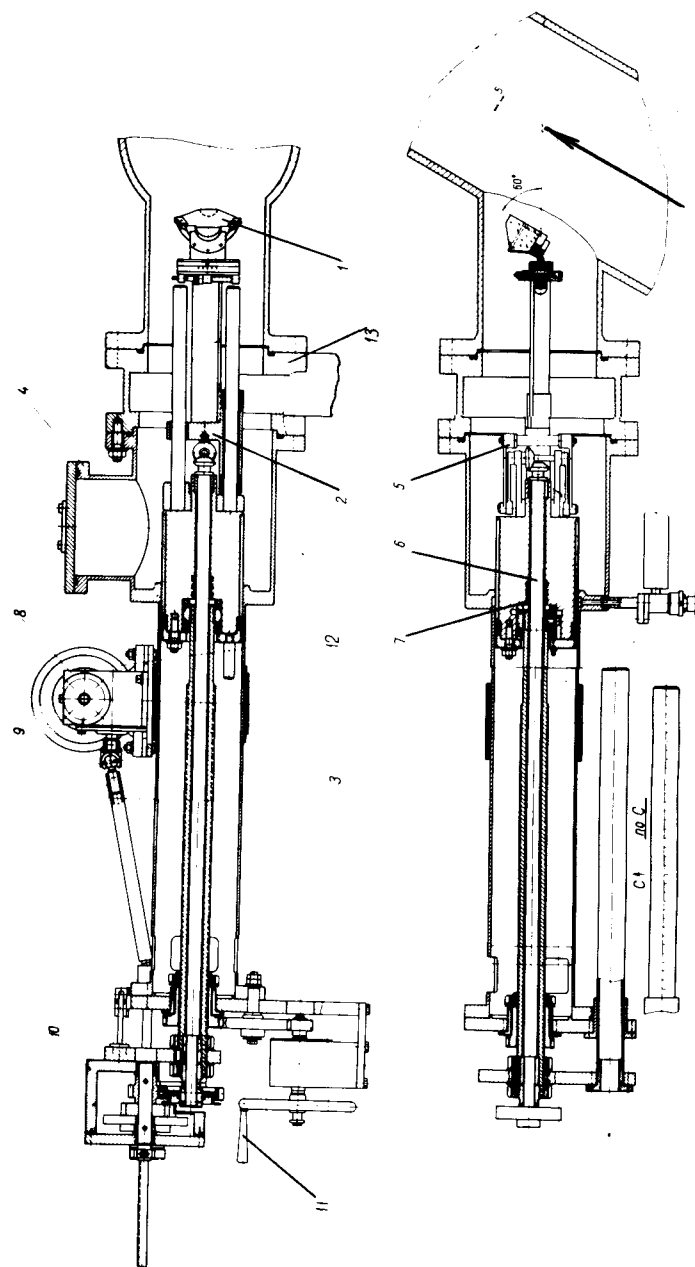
Механизм ввода мишени: 1 - мишень-радиатор; 2 - ползун; 3 - силовой шток механизма ввода (ход 340 мм); 4 - шлюз для смены мишени; 5 - шатун; 6 - приводной вал кривошипно-шатунного механизма; 7 - уплотняющие резиновые кольца; 8 - редуктор; 9 - карданный вал; 10 - редуктор с безударным механизмом; 11 - ручной привод механизма ввода; 12 - электродвигатель возвратно-поступательного механизма мишени (ход 114 мм); 13 - вакуумный шибер.
